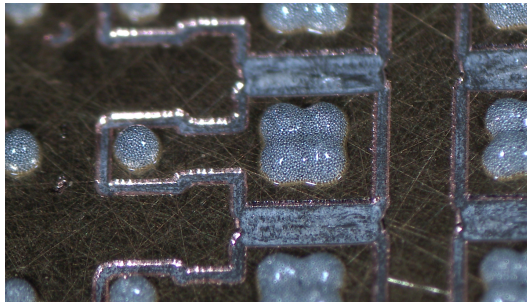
Detalle dispensación pasta de soldadura sobre los pads.
